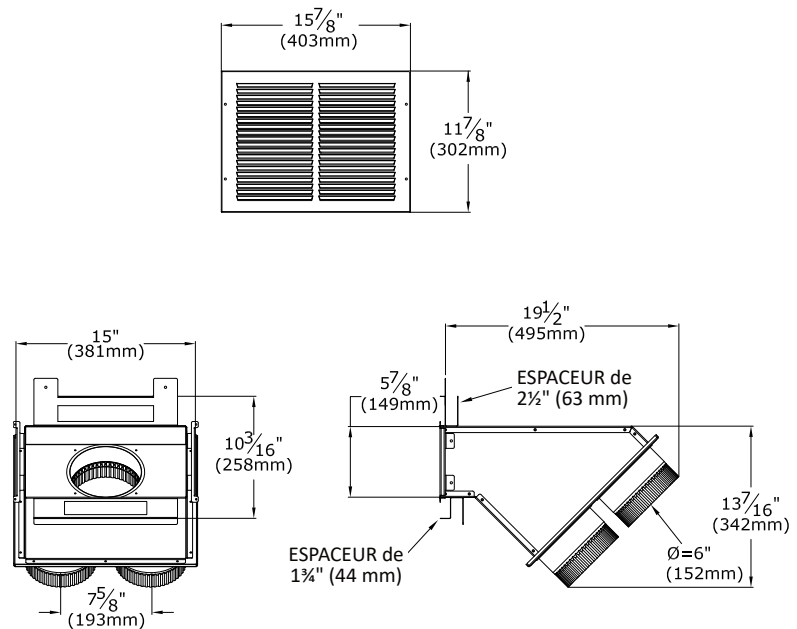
Vue d'ensemble du kit KZK-1510
